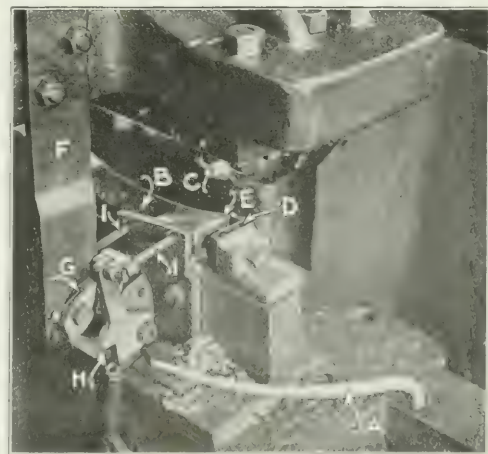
TROQUEL PARA CHAVETAS CON DESAJADOR AUTOMÁTICO
